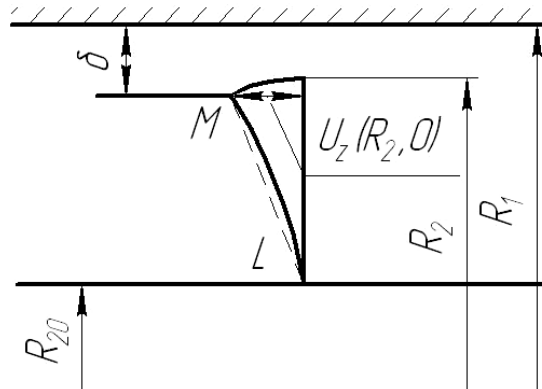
Схема корпуса вовчка зі шнеком
